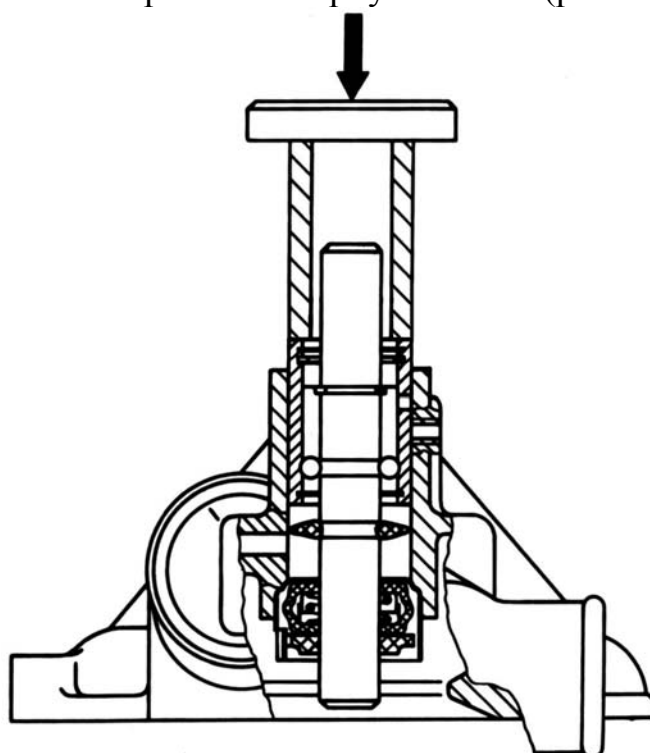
Запрессовка подшипника с валиком насоса
